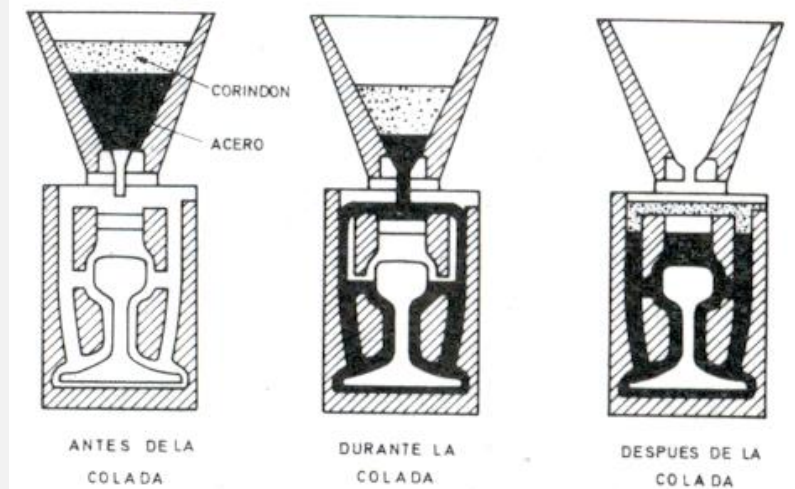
Soldadura aluminotérmica, colada.
